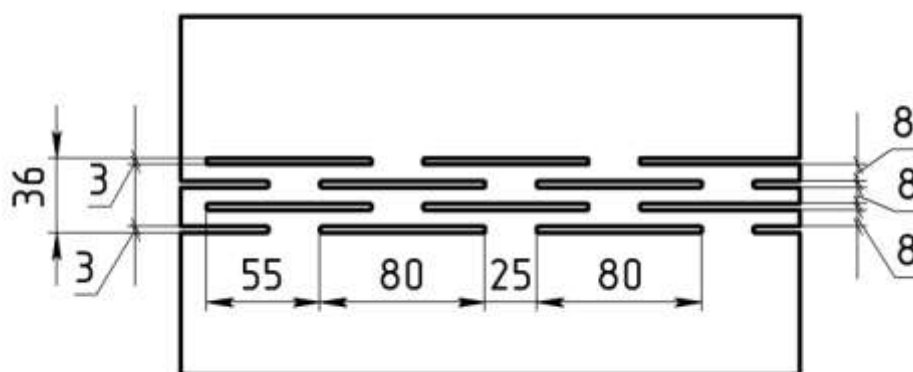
Схема расположения просечек на стенке термопрофиля TRS-080-125
